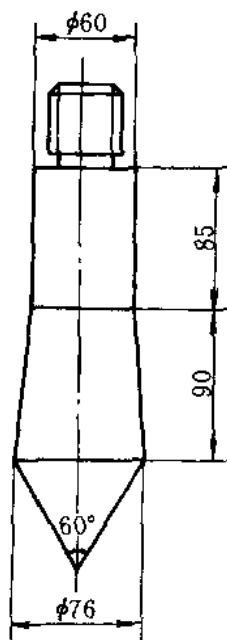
重型、超重型动力触探探头 (单位: mm)
